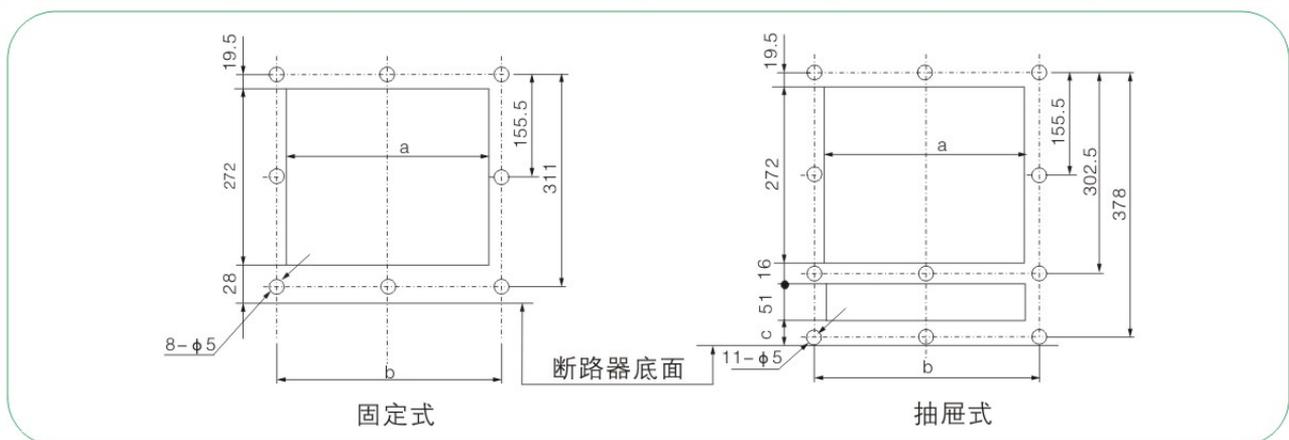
抽屉式断路器安装尺寸及外形尺寸 (ZHW1-6300/4 In=6300A)
